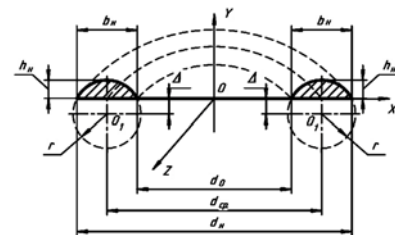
Схематичное представление диаметрального сечения напльвов металла и форма образуемой ими поверхности по краю лунки
